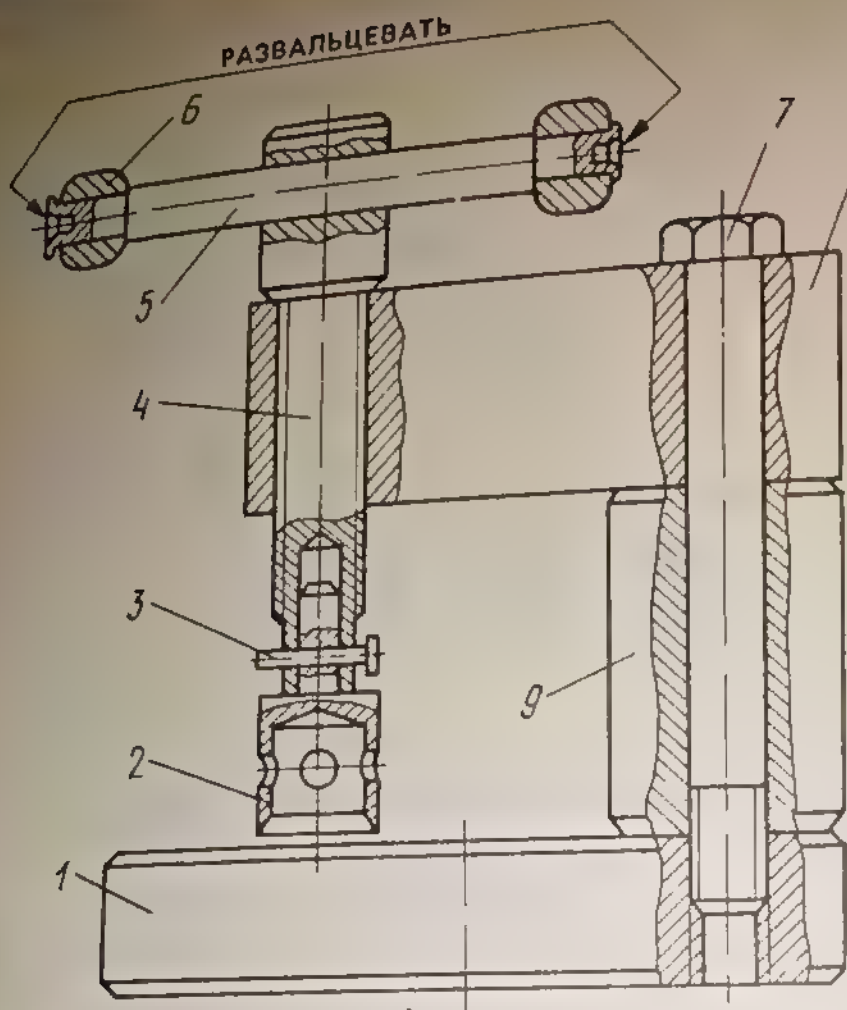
Приспособление для вырезания из листового эластичного материала уплотняющих прокладок и уплотнительных колец прямоугольного сечения
